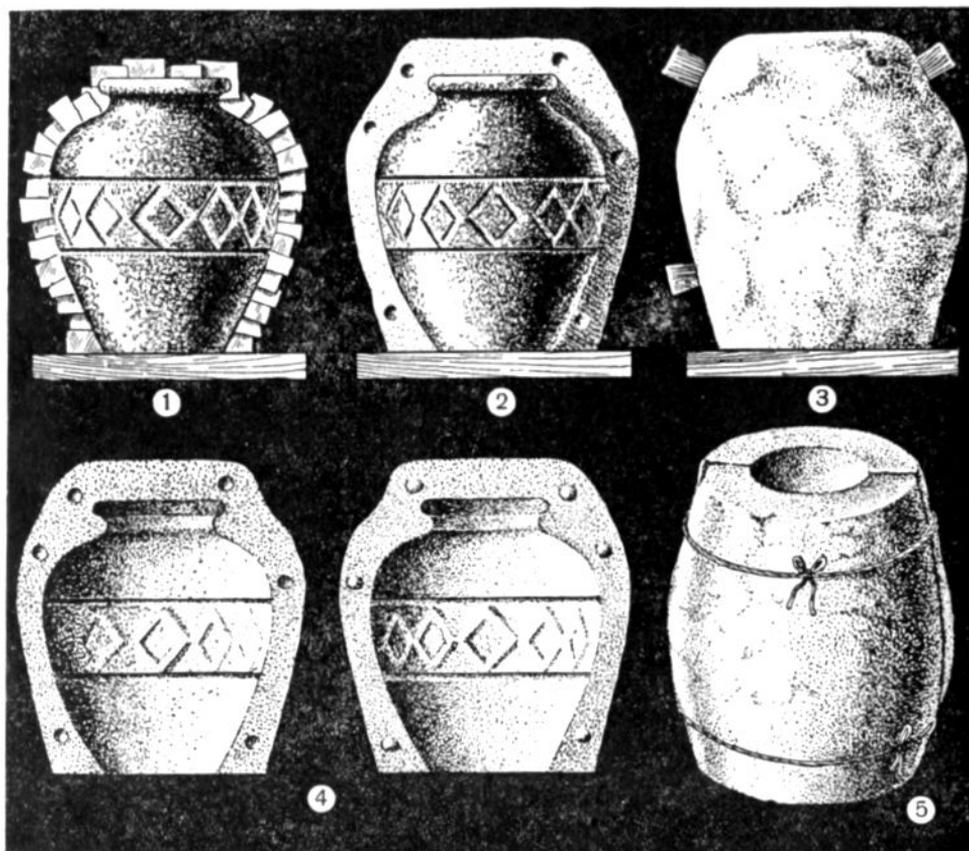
Последовательное изготовление черновой формы с объемной модели: 1 — постановка пластинок; 2 — первая половина формы; 3 — разъемка половинок формы; 4 — половинки формы; 5 — общий вид формы, подготовленной для отливки.
